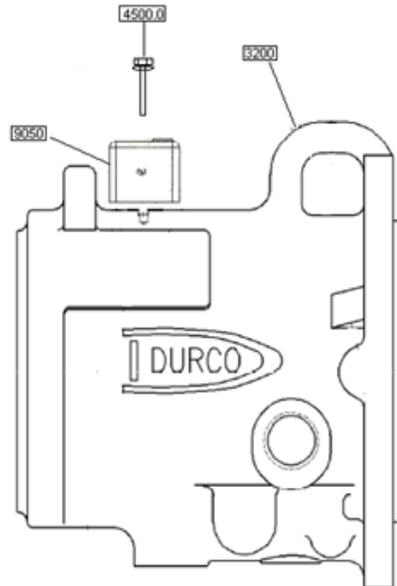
exemple de plan d'installation IPS Beacon sur une pompe Durco
